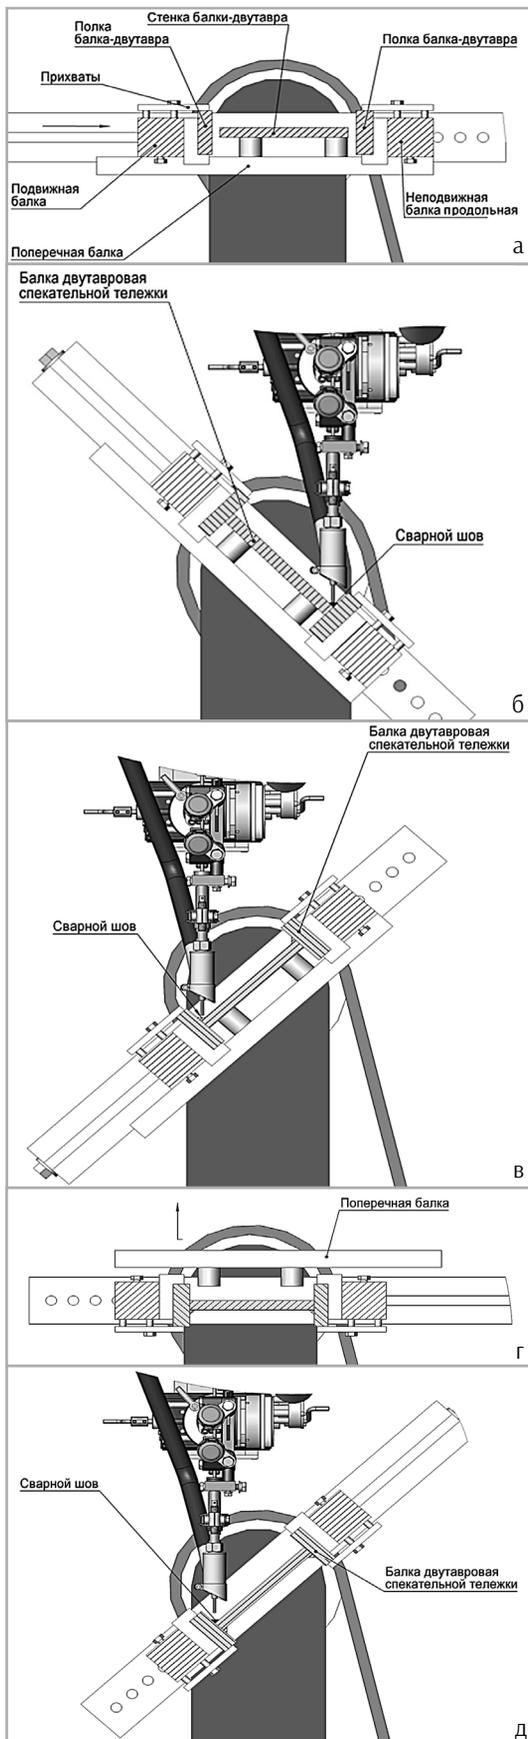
Последовательность сборки и сварки двутавровых балок на специализированной установке: а, г – сборка; б, в, д – сварка
